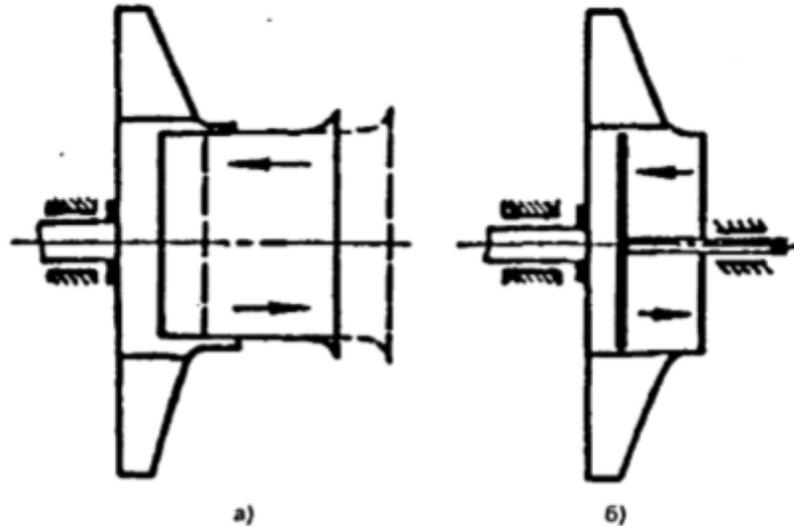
Схемы регулирующих устройств: а – с подвижным цилиндрическим кольцом; б – с передвижным диском
